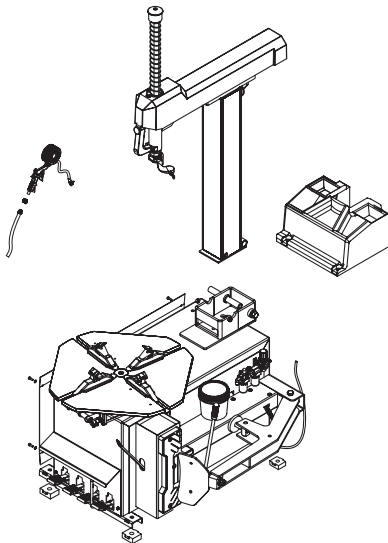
Монтаж стойки шиномонтажного стенда
